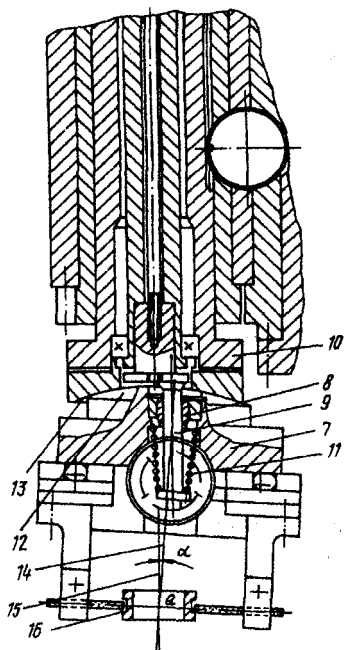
Конструкция инструментальной головки с вертикальным расположением оси
